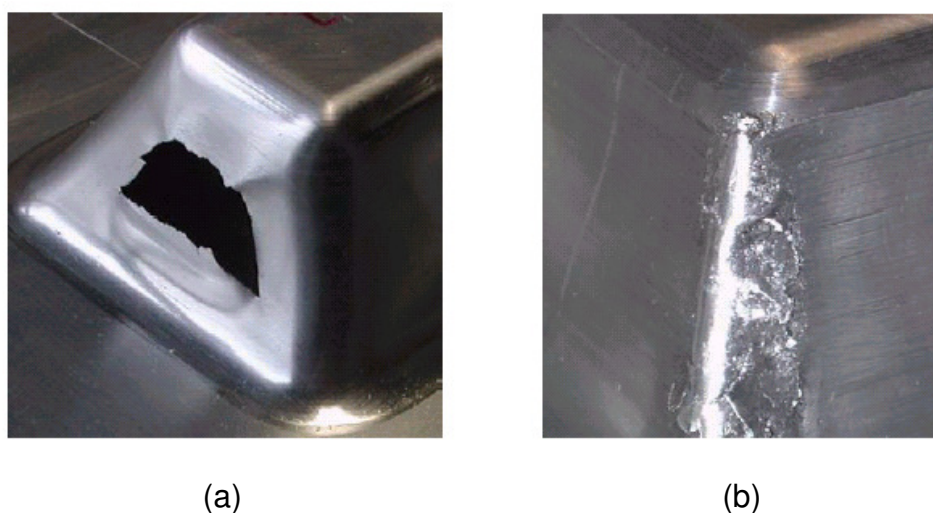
Limites de estampagem em ISF: a - falha dúctil sobre passes do flange, b - desgaste da superfície em estampagem multiestágio (Hirt et al., 2003).
